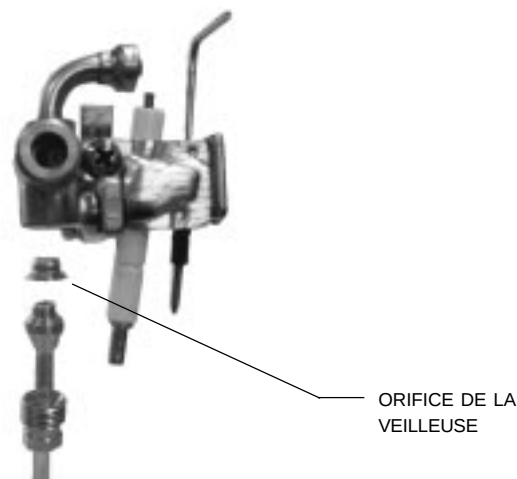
Brûleur et orifice de la veilleuse (assemblage illustré sans le capuchon de la veilleuse)
